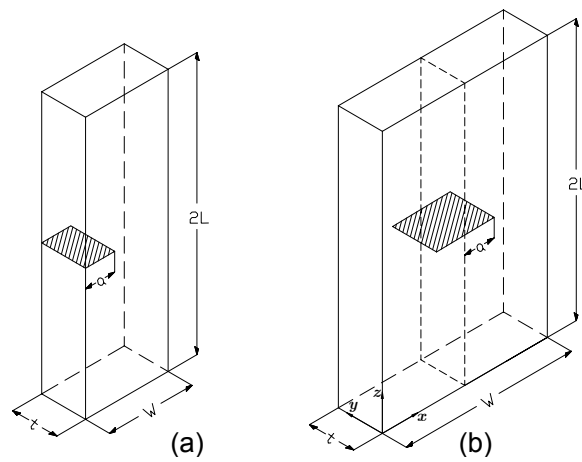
Esquema probeta gruesa, (a) grieta sobre un borde libre, (b) grieta interna.
